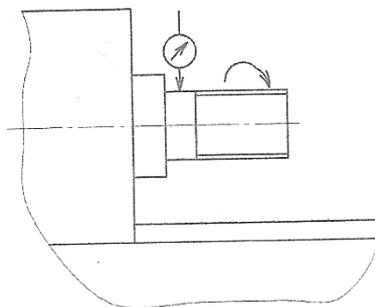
Схема установки индикатора для проверки радиального биения, центрирующей шейки шпинделя
